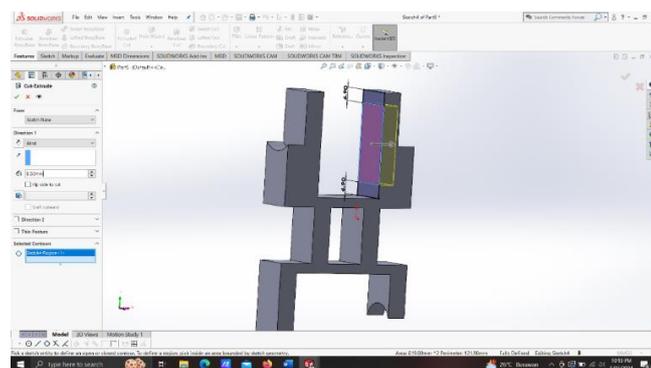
Hasil *Extruded Cut* Pada Sisi Samping Kiri
